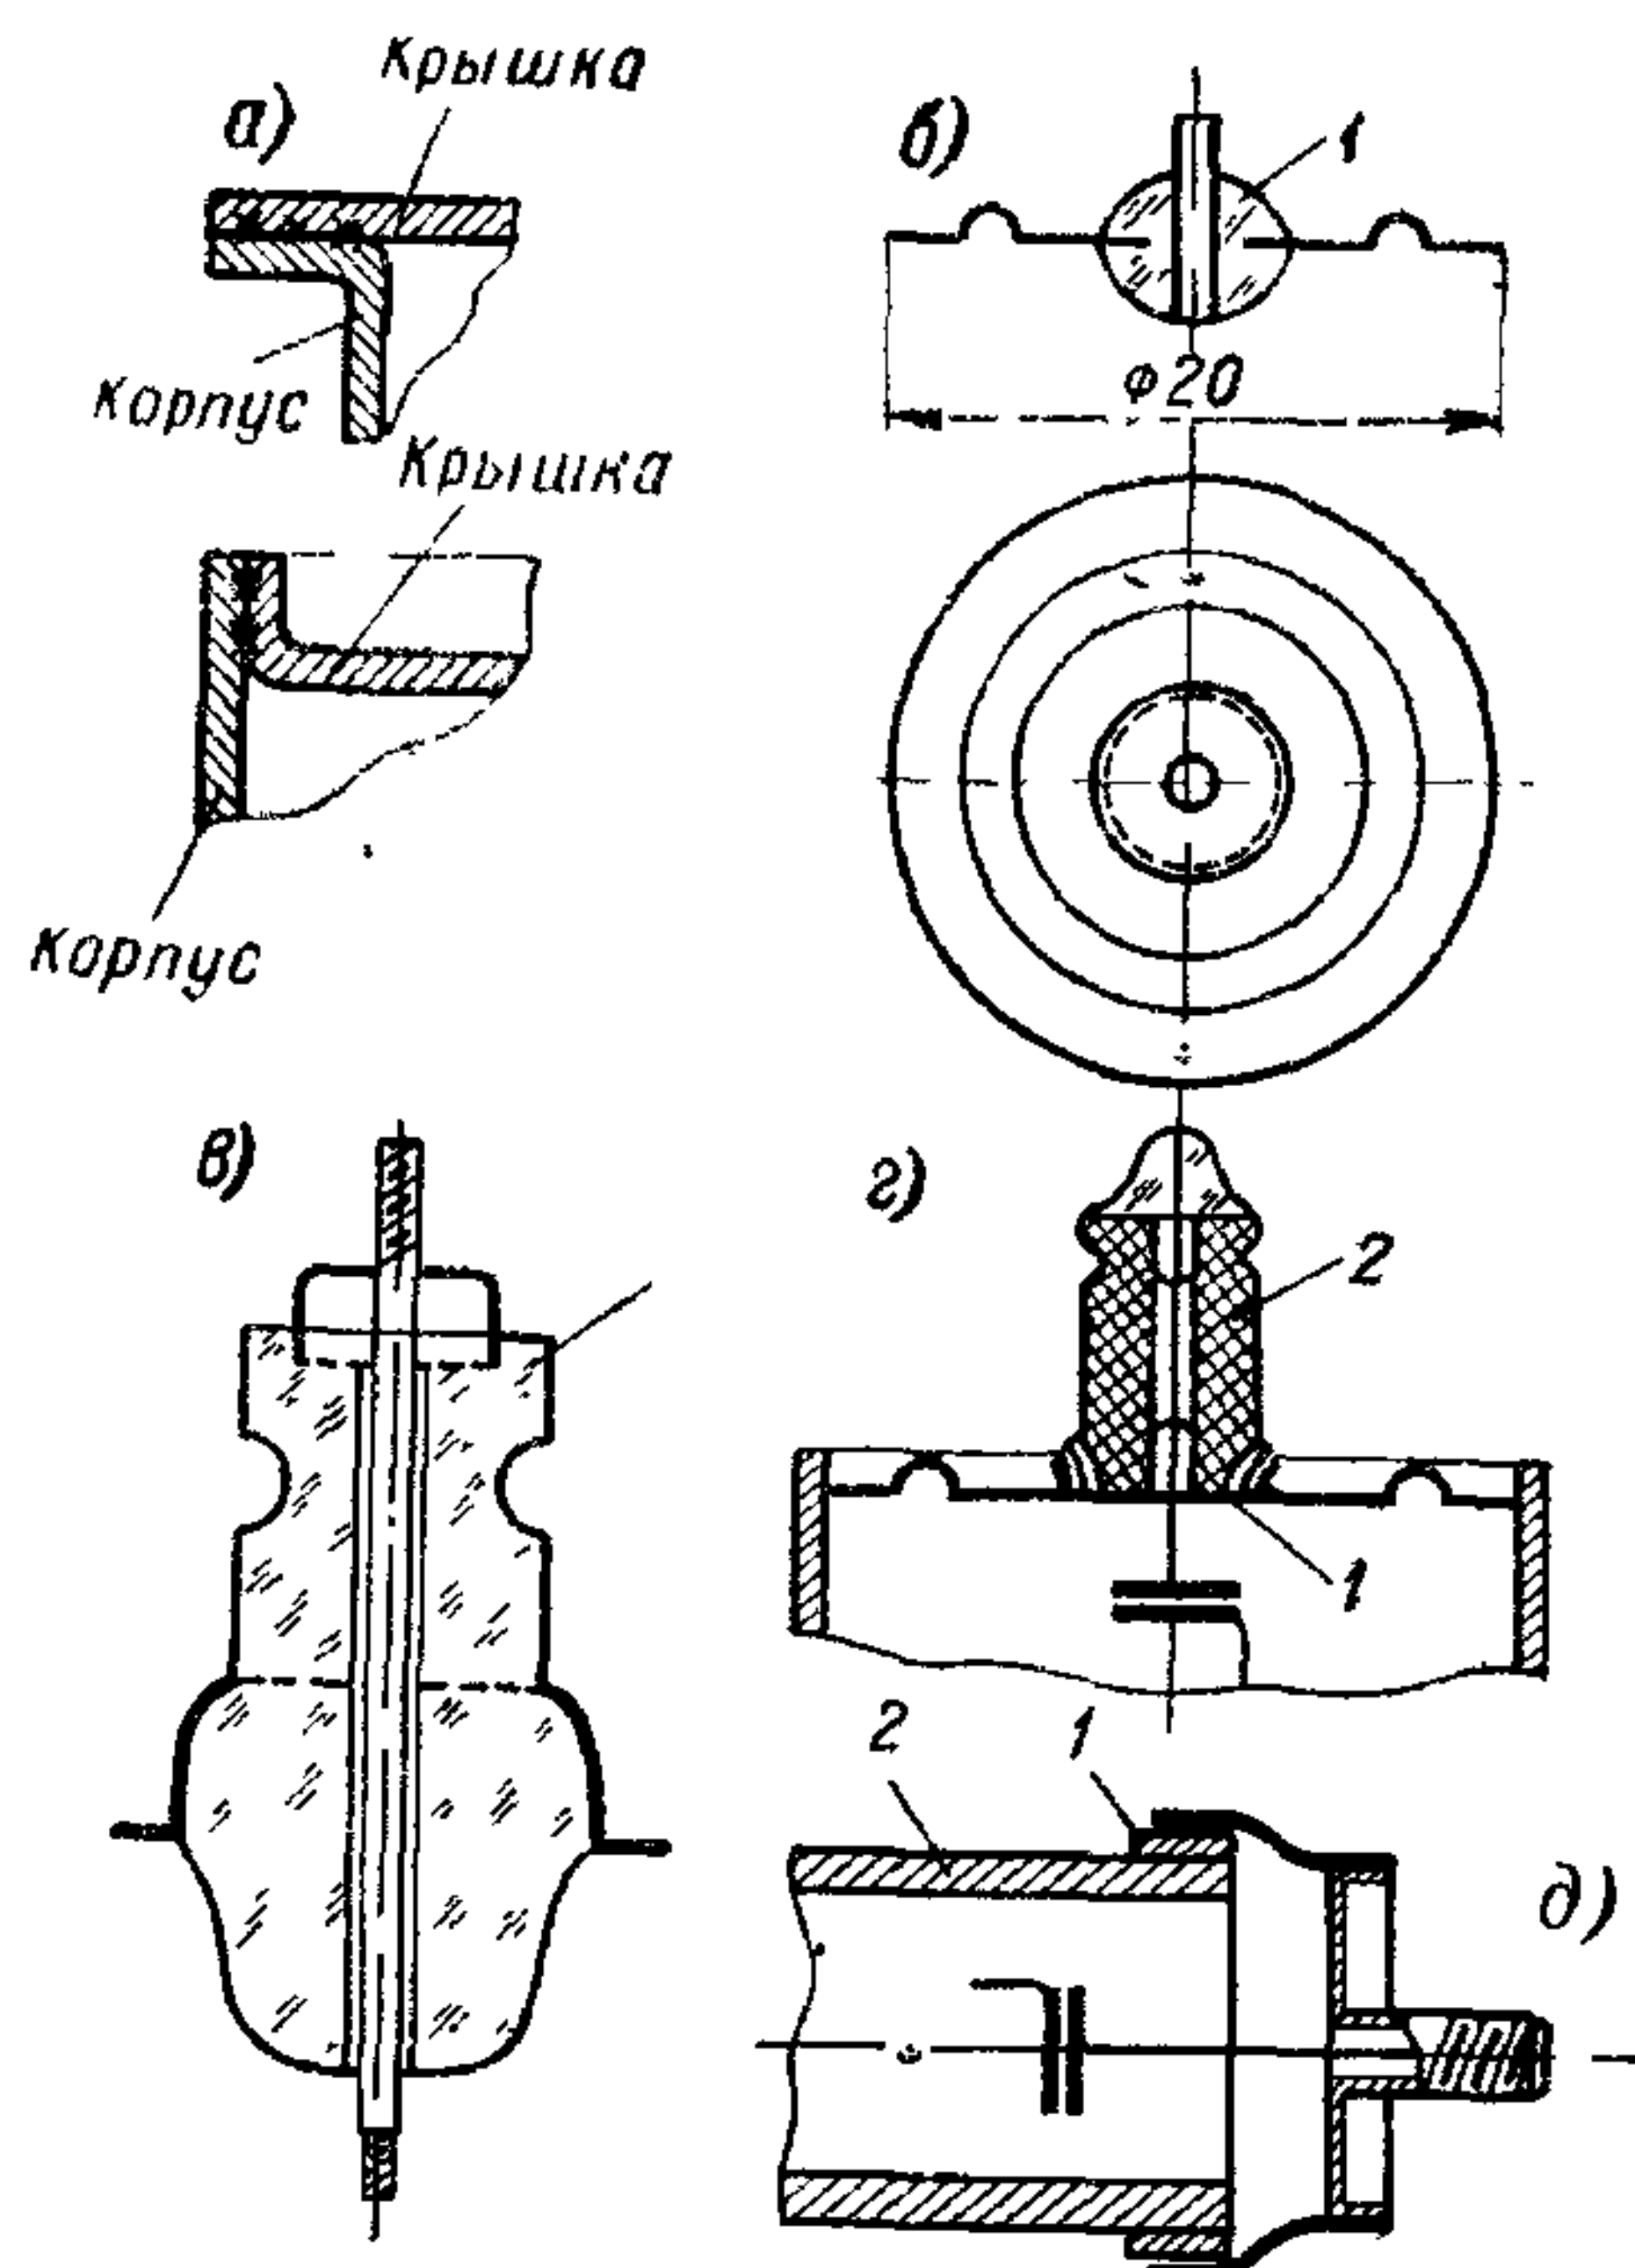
Система герметизации для нагревостойких конденсаторов: а — методы сварки крышки с корпусом (вверху — рельефный, внизу — дуговой); б — стеклянный низковольтный изолятор, допускающий приварку шайбы к крышке корпуса; в — стеклянный высоковольтный изолятор, допускающий приварку или пайку твердым припоем; г — керамический изолятор, соединенный с крышкой переходным слоем стекла (крышка сварена с корпусом); д — керамическая трубка (корпус) переходным слоем стекла соединена с коваровым кольцом; к кольцу приварена стальная крышка (1 — стекло; 2 — керамика).
